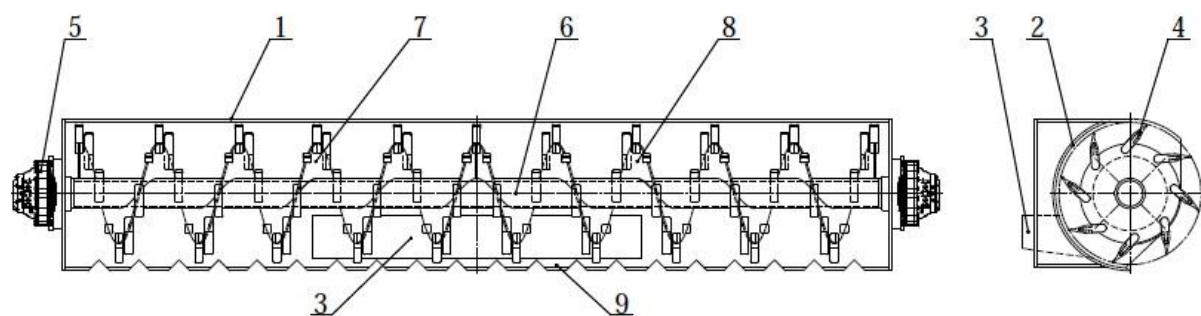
Грунтозаборное устройство фрезерно-шнекового типа для сплошного фрезерования обводненной торфяной залежи
